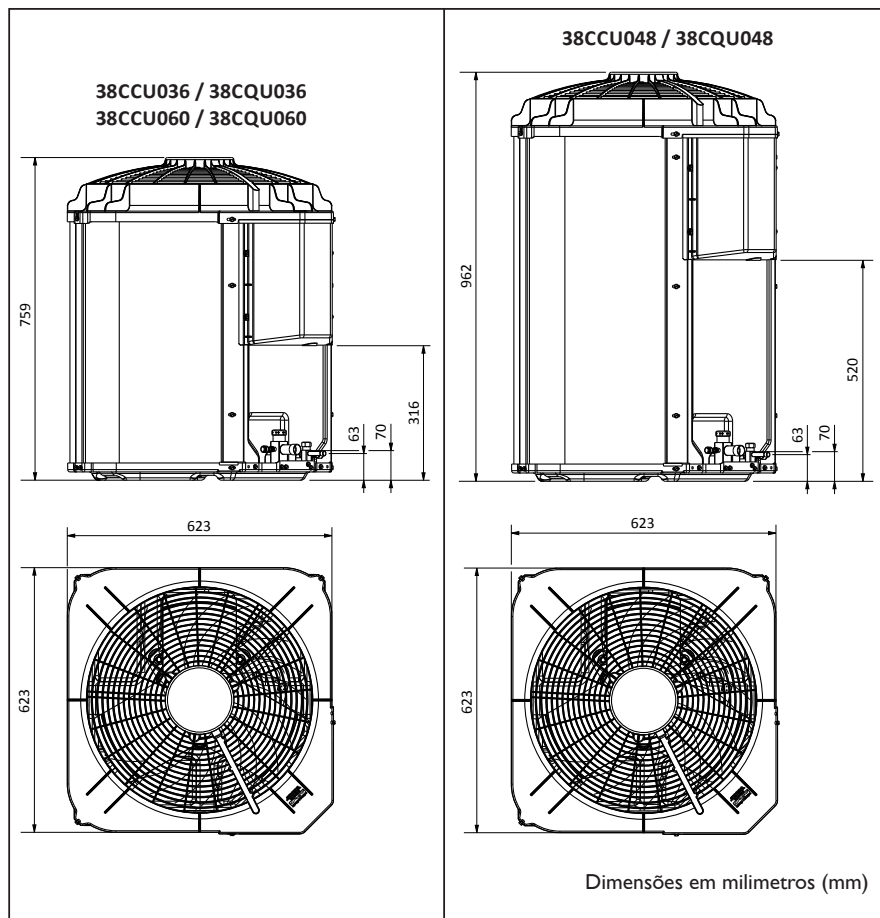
DIMENSIONAL UNIDADES CONDENSADORAS 38C
